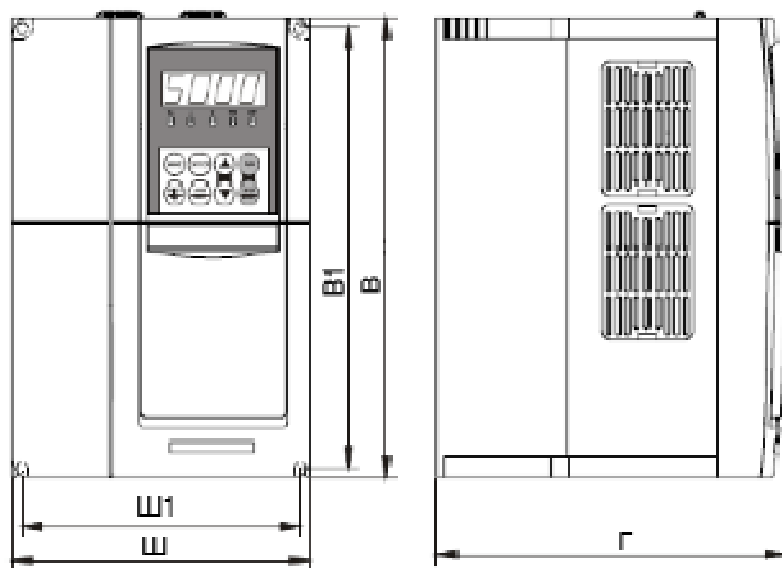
Габаритный чертёж преобразователя частоты модели А
